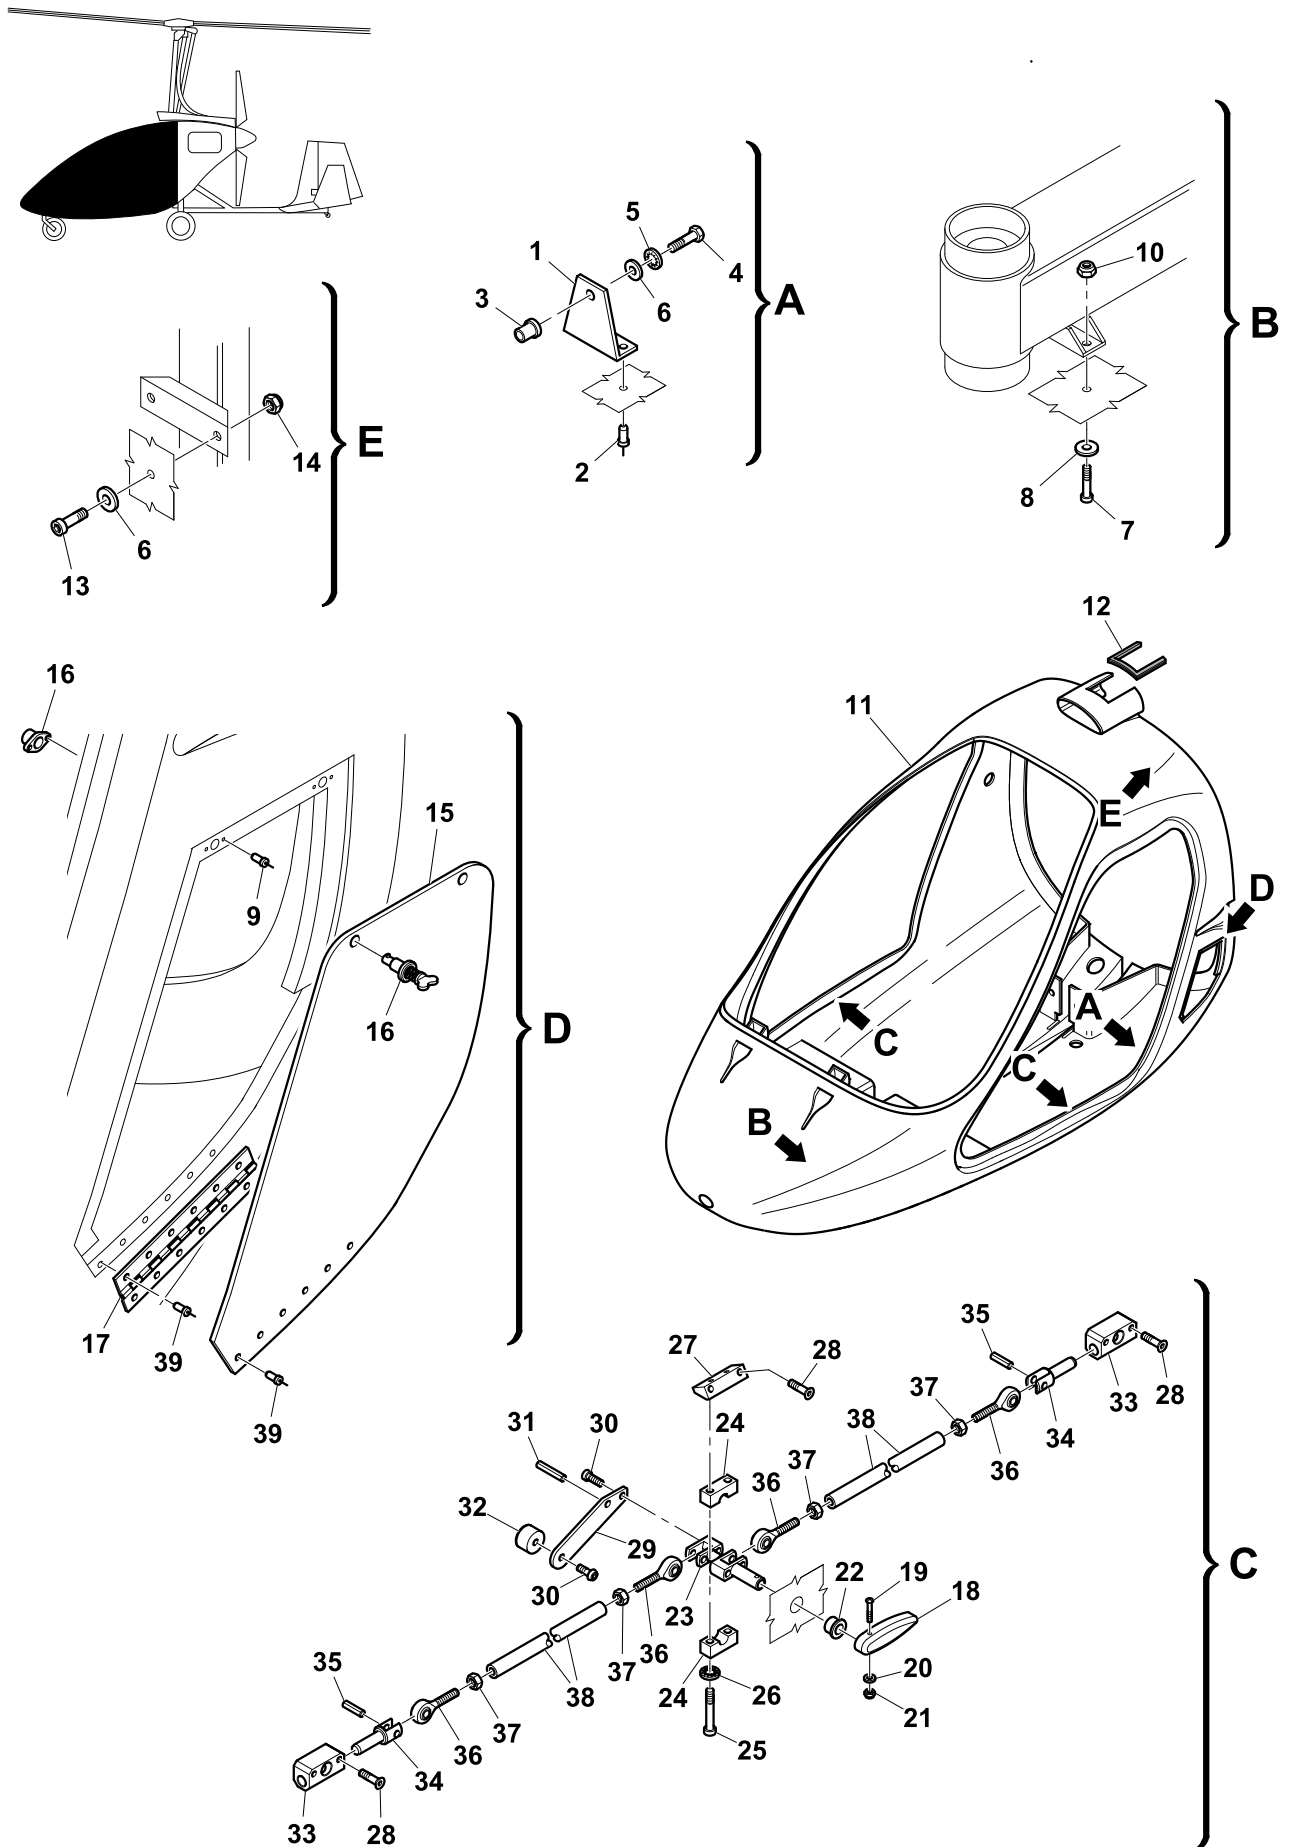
CABINA 2^a parteFIG. 08b - COCKPIT 2nd part
